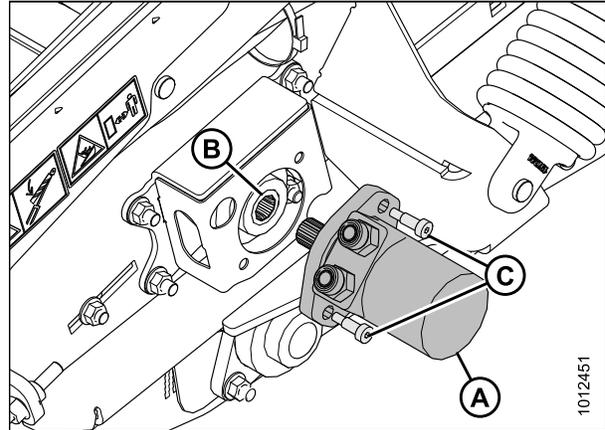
Motor hidráulico delantero; lado izquierdo
